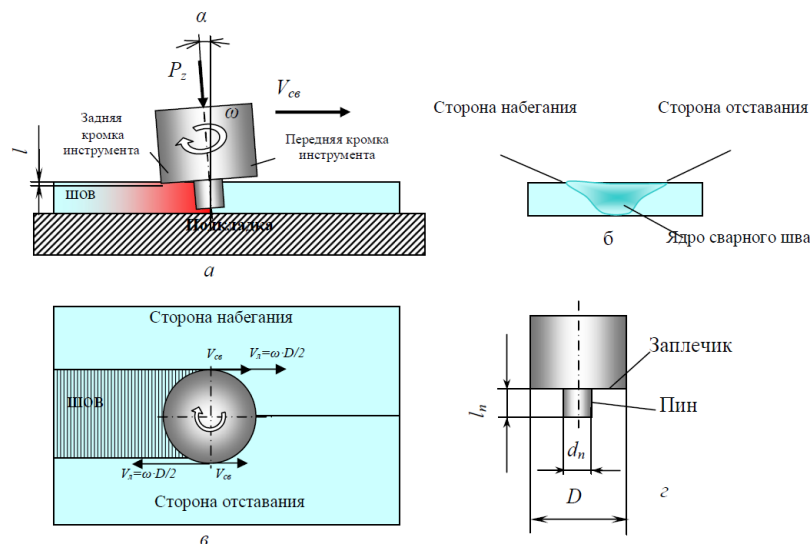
Сущность сварки трением с перемешиванием:
